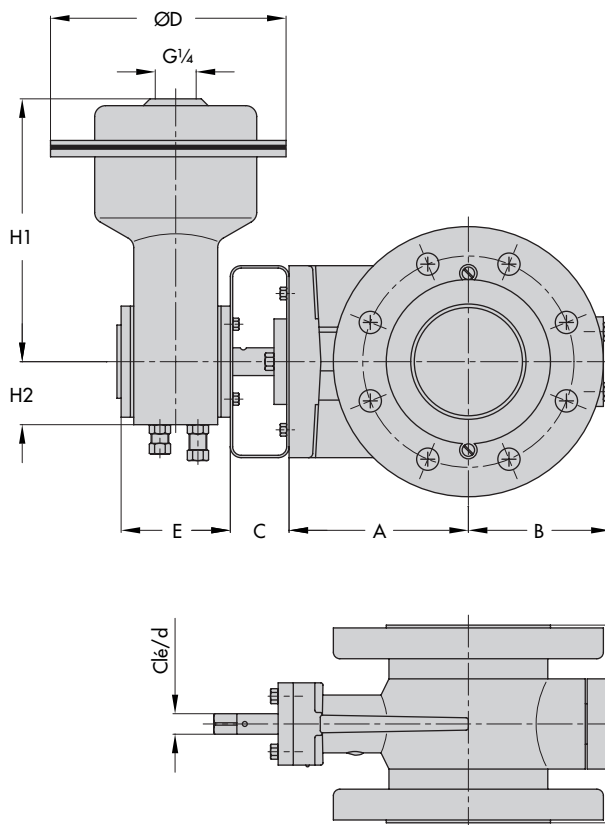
· Schéma de la vanne type 3310/3278 (voir dimensions tableau 7)
